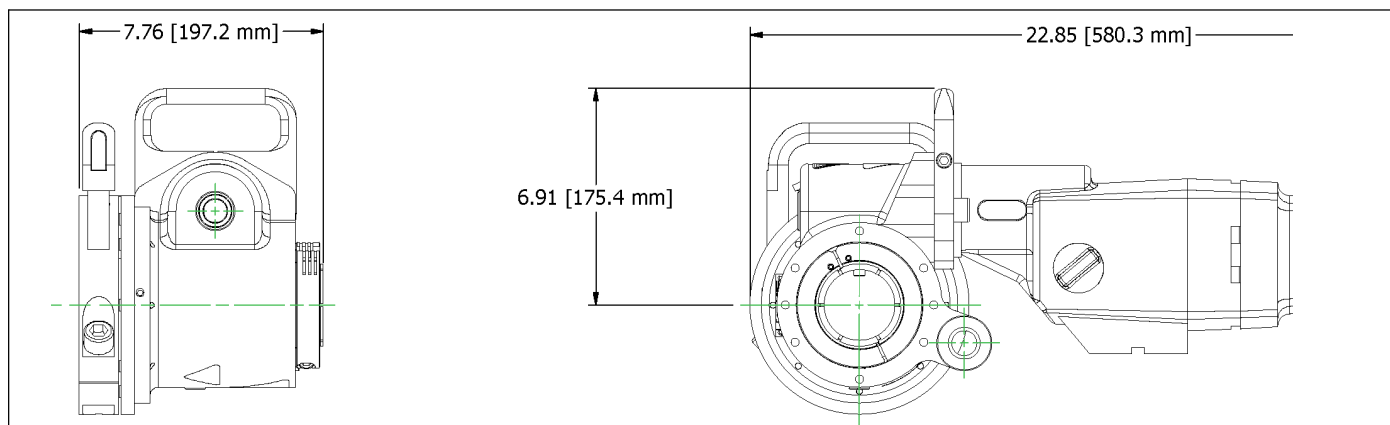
DIMENSIONS DU MOTEUR EIBENSTOCK ET RDU
